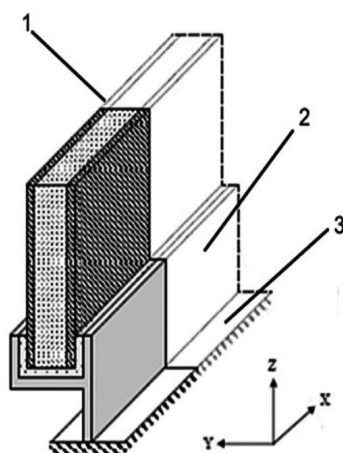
Соединение надстройки из ПКМ с основным металлическим корпусом судна:
